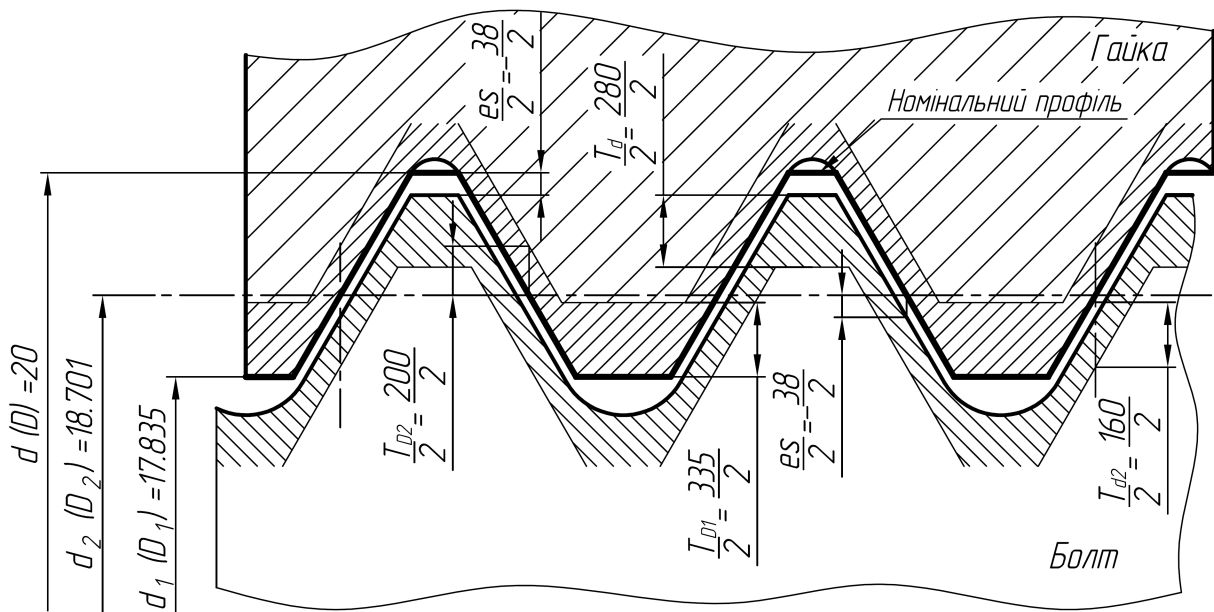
Схема розташування полів допусків різьбового з'єднання $M20 \times 2 - 6H/6g$
